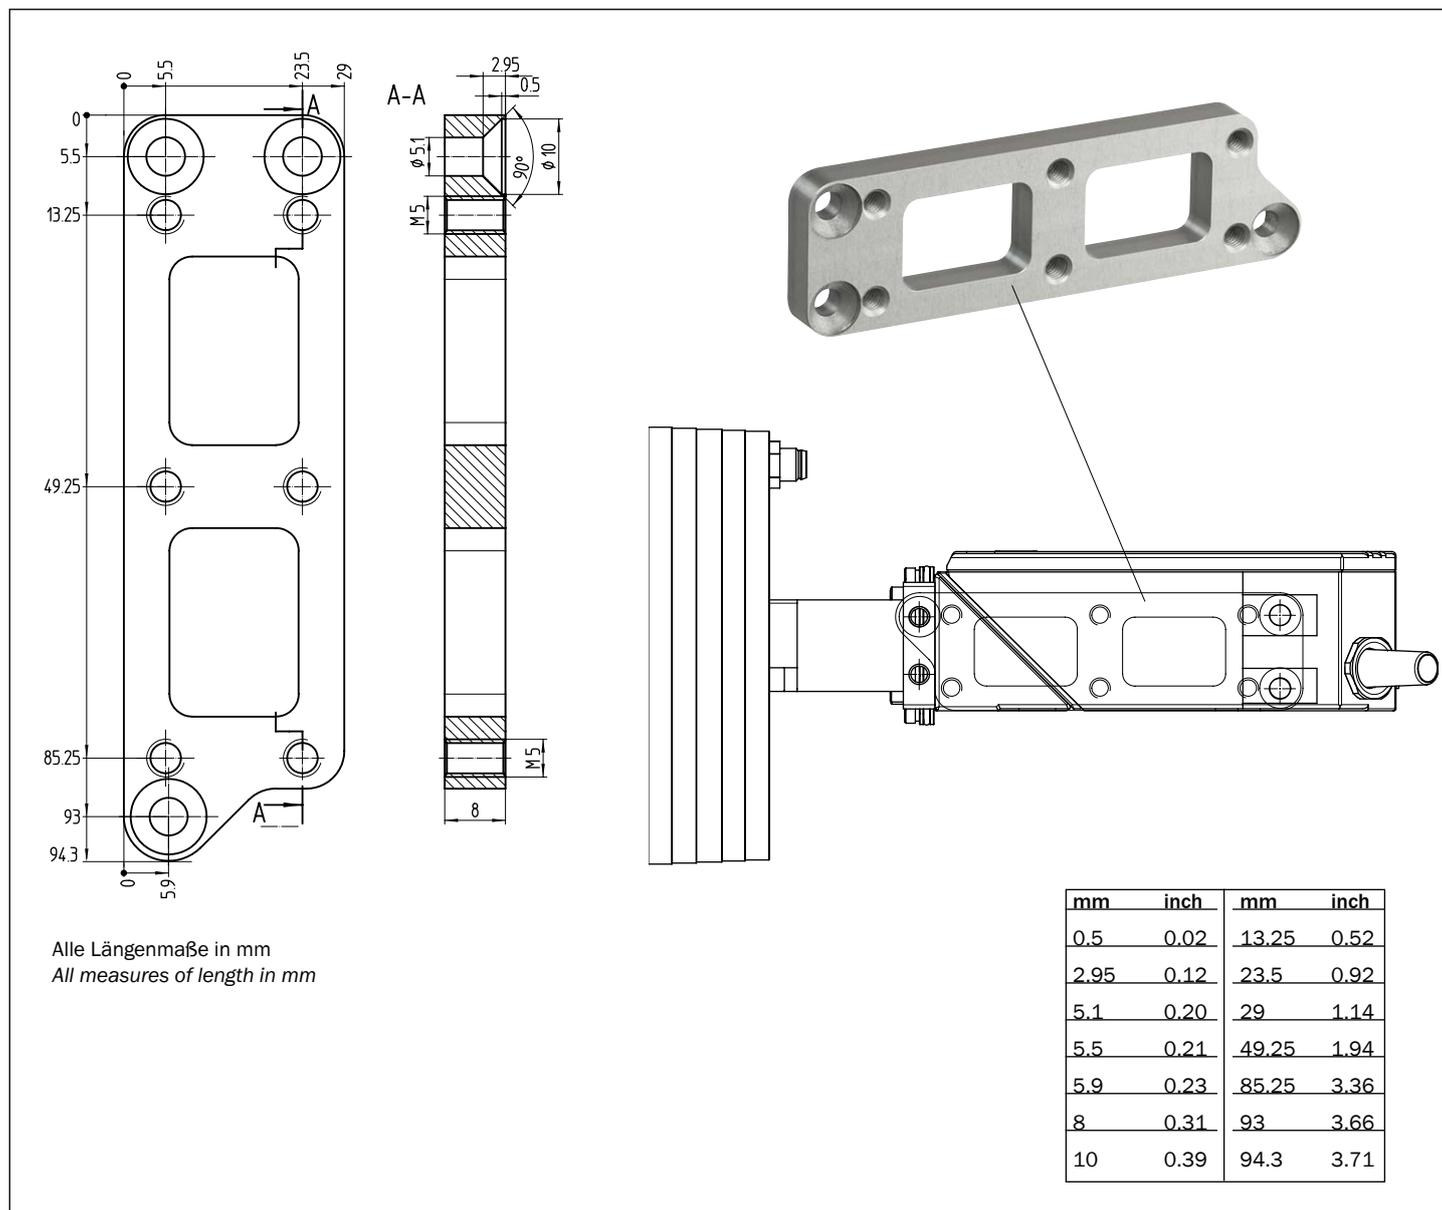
Abmessungen der Montageplatte Artikel-Nr. 2050691 für Ringbeleuchtungen ICL170, ICL260, ICL280, ICL300 und ICR845-2L0020 FlexLens
